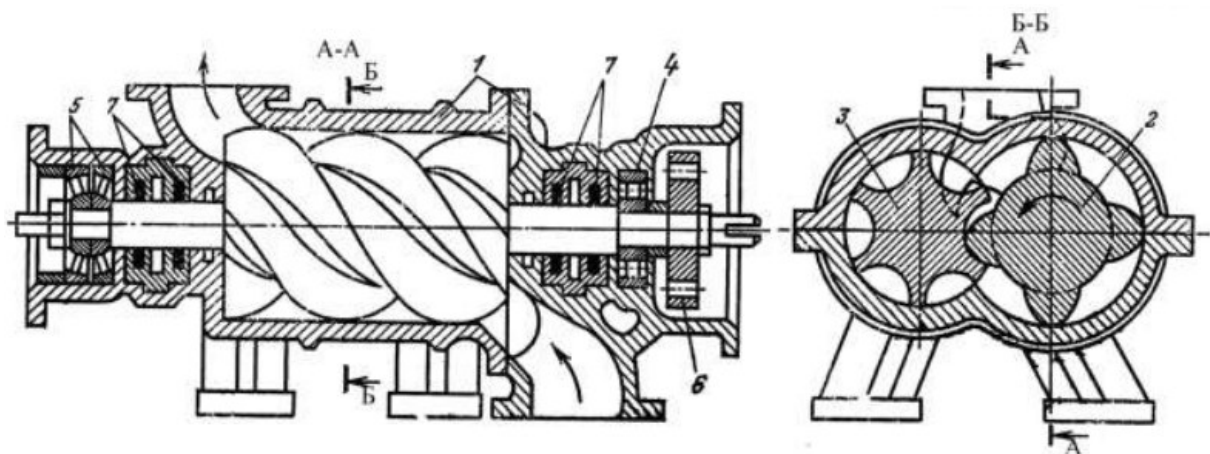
Схема гвинтового компресора: 1 – корпус; 2 – ведучий ротор; 3 – ведений ротор; 4,5 – підшипники ротора; 6 – шестерня; 7 – ущільнення.
